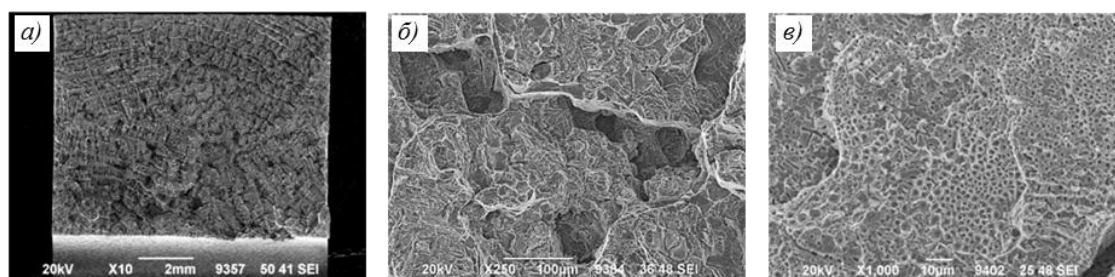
Строение излома образца при сочетании материалов «отливка + отливка»:
